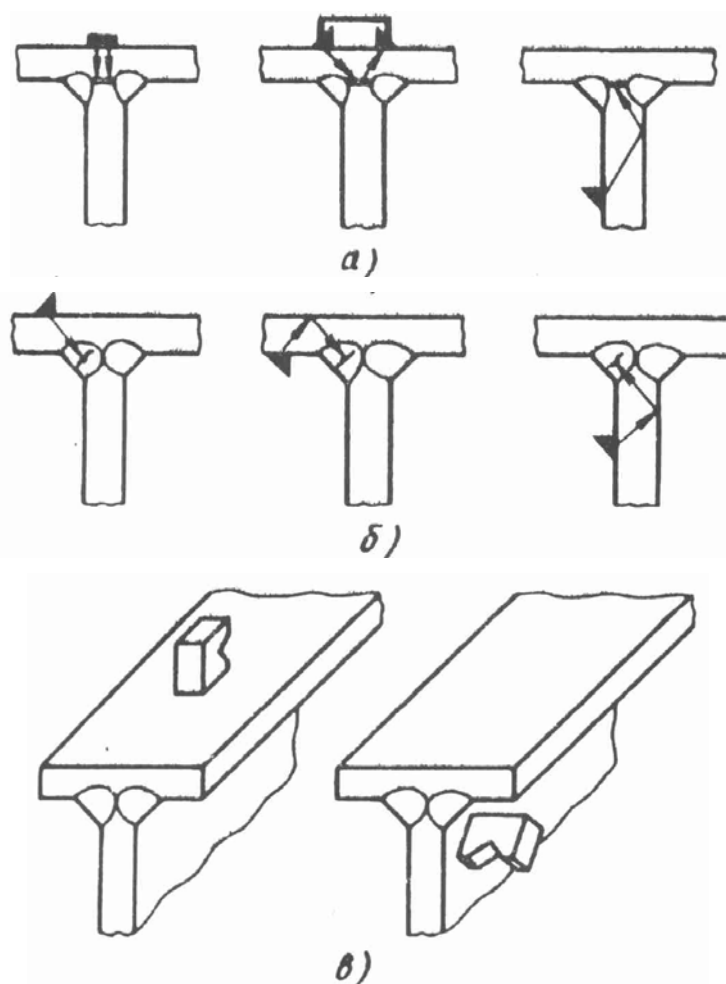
Схемы контроля тавровых сварных соединений при выявлении дефектов: а – непровара в корне шва; б – продольных трещин, пор и шлака; в – поперечных трещин
